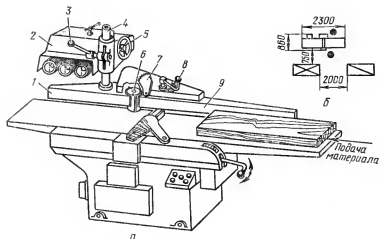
Станок двусторонний фуговальный с горизонтальным и вертикальным шпинделями С2ФЗ-2 (а) и организация рабочего места (б):
